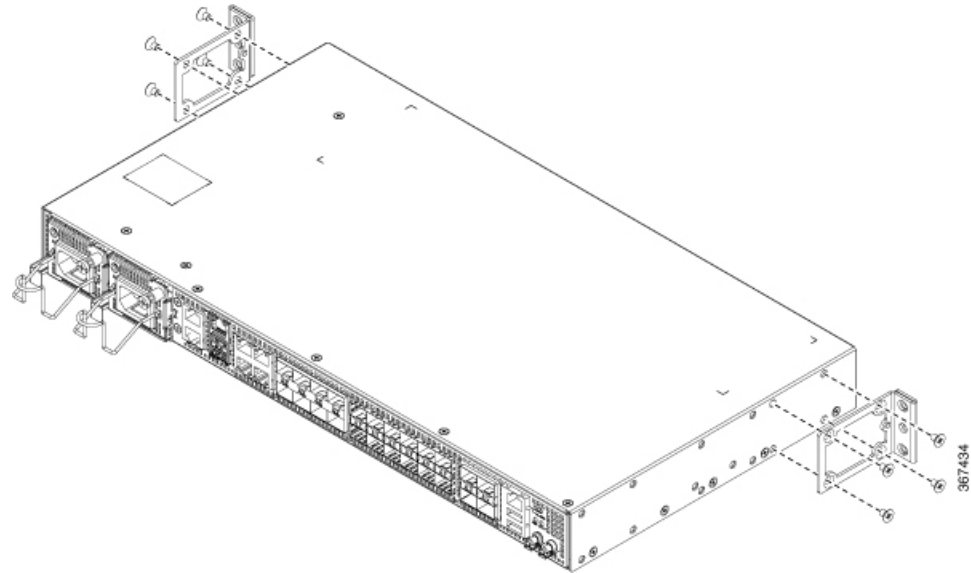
Fixar os suportes de montagem no router para rack EIA de 23 polegadas (posição frontal)
